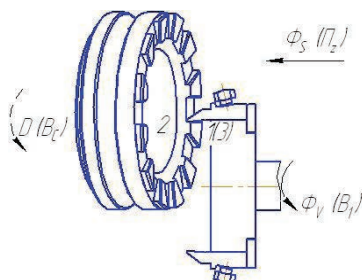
Общий вид фрезерования зубьев по методу 3
